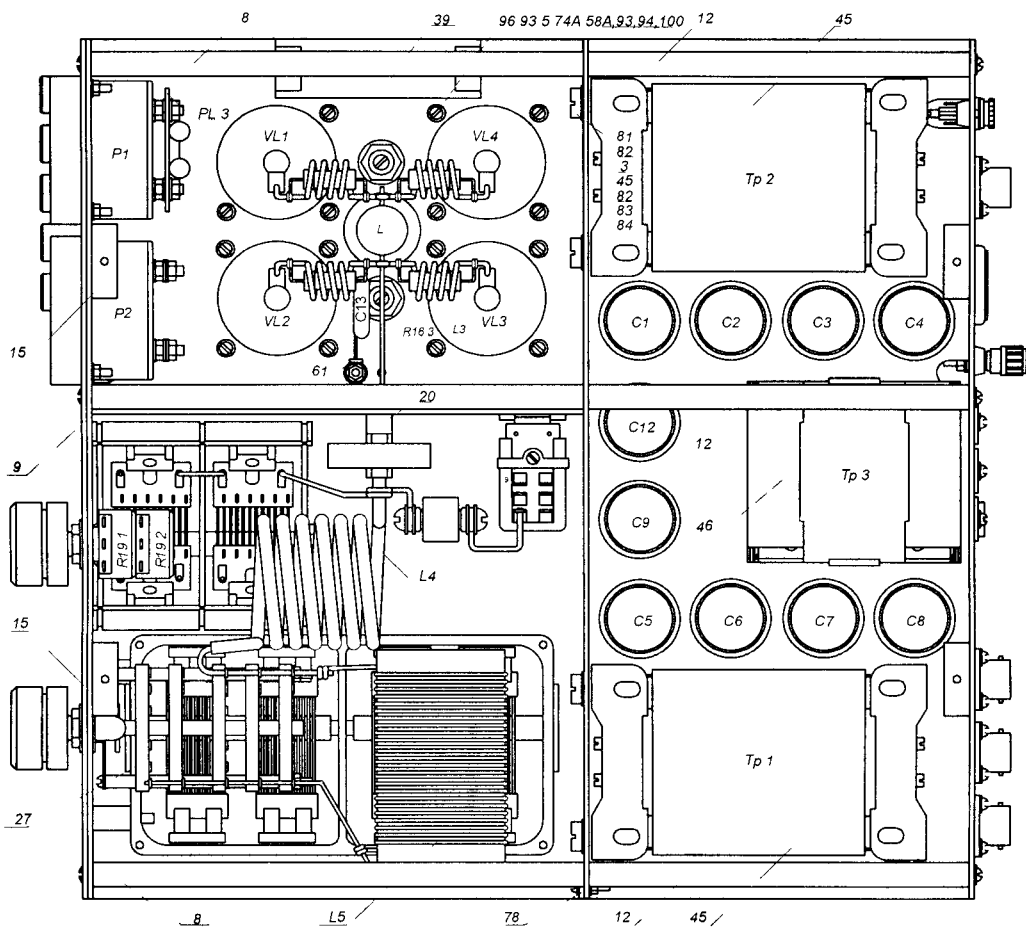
Е Сборочный чертеж усилителя DVA-300E Вид сверху со снятой верхней крышкой
